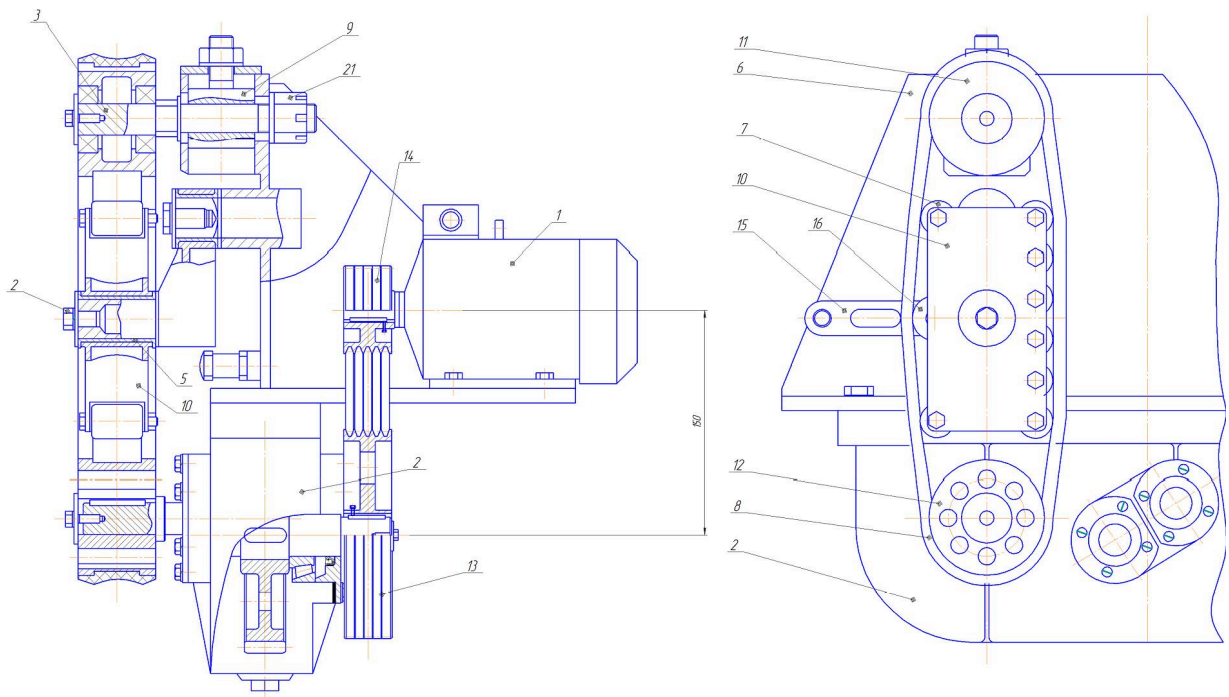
Пристрій призначений для протягування плівки: 1 – мотор; 2 – редуктор; 3 – кожух; 4 – корпус; 5 – ролики; 6 – протягуючий пас; 7 повзун; 8 – тримач для роликів; 9 – верхній шків; 10 – нижній шків; 11 – редукторний шків; 12 – шків двигуна; 13 – планка; 14 – натяжний пристрій
